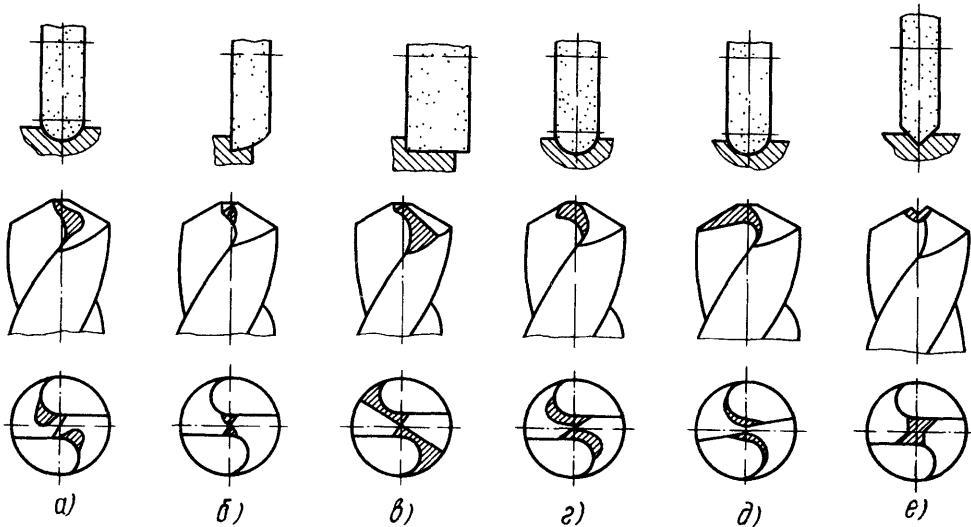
Способы подточки поперечной режущей кромки сверла
